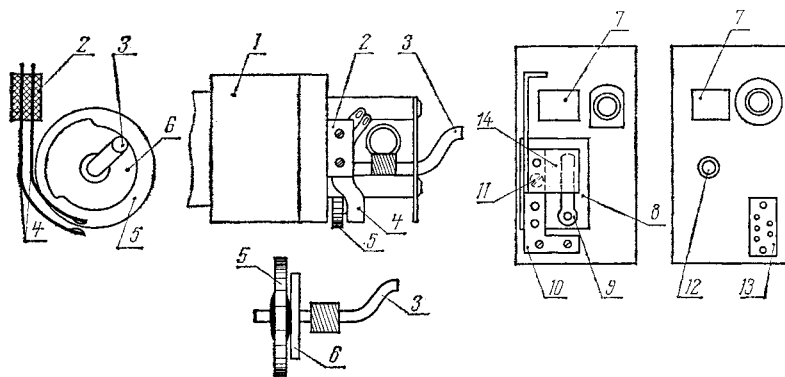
Доработка кинокамеры «Спорт»: 1 — корпус электродвигателя; 2 — изоляционные прокладки, гетинакс; 3 — коленчатый вал грейфера; 4 — контакты (КГК1); 5 — большая шестерня; 6 — кулачок, гетинакс; 7 — видеоискатель; 8 — пластина, текстолит; 9 — контакты выключателя электродвигателя (П-В1); 10 — стопорная планка грейферного механизма; 11 — винт М3; 12 — кнопка включения кинокамеры («Пуск»); 13 — штепсельный разъем Ш3; 14 — изоляционная пластина.
